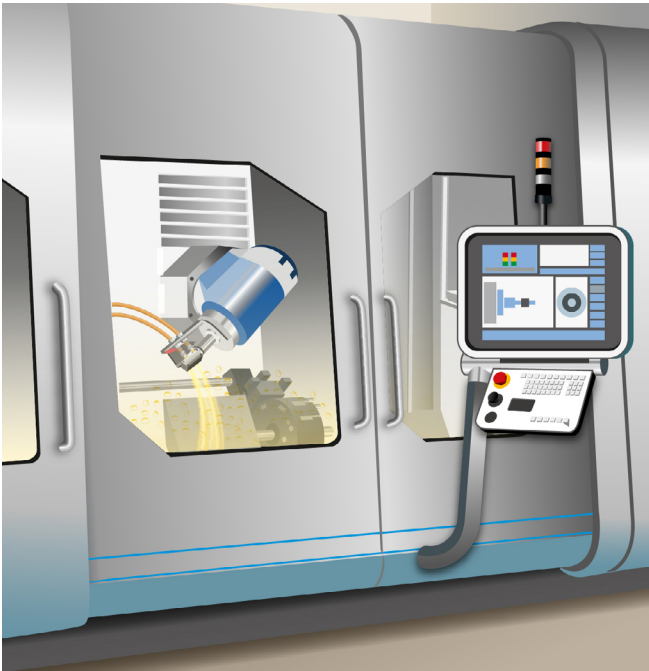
Nassbearbeitung in einer CNC-Schleifmaschine
